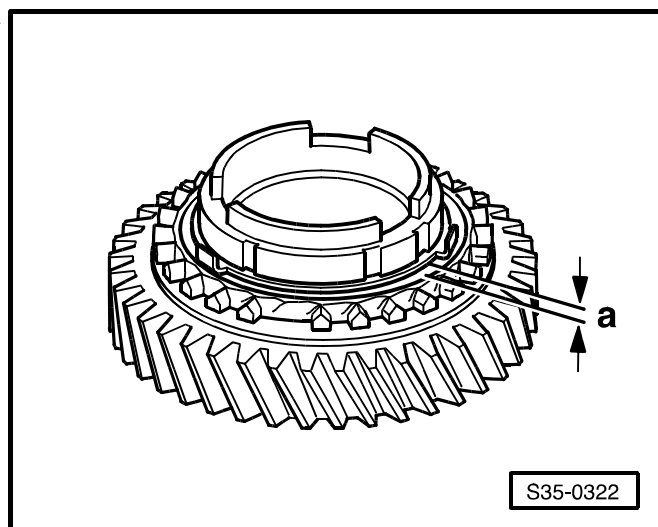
Контроль износа блокирующих колец синхронизатора для 1-ой, 2-ой и 3-ей передач
